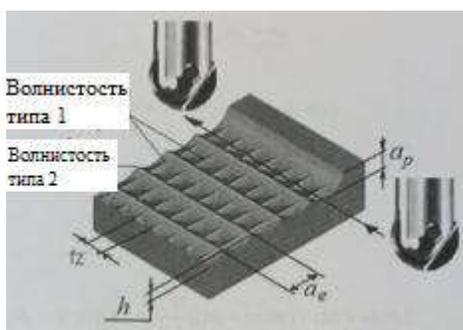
Образование гребней после фрезерования сфероцилиндрической фрезой
